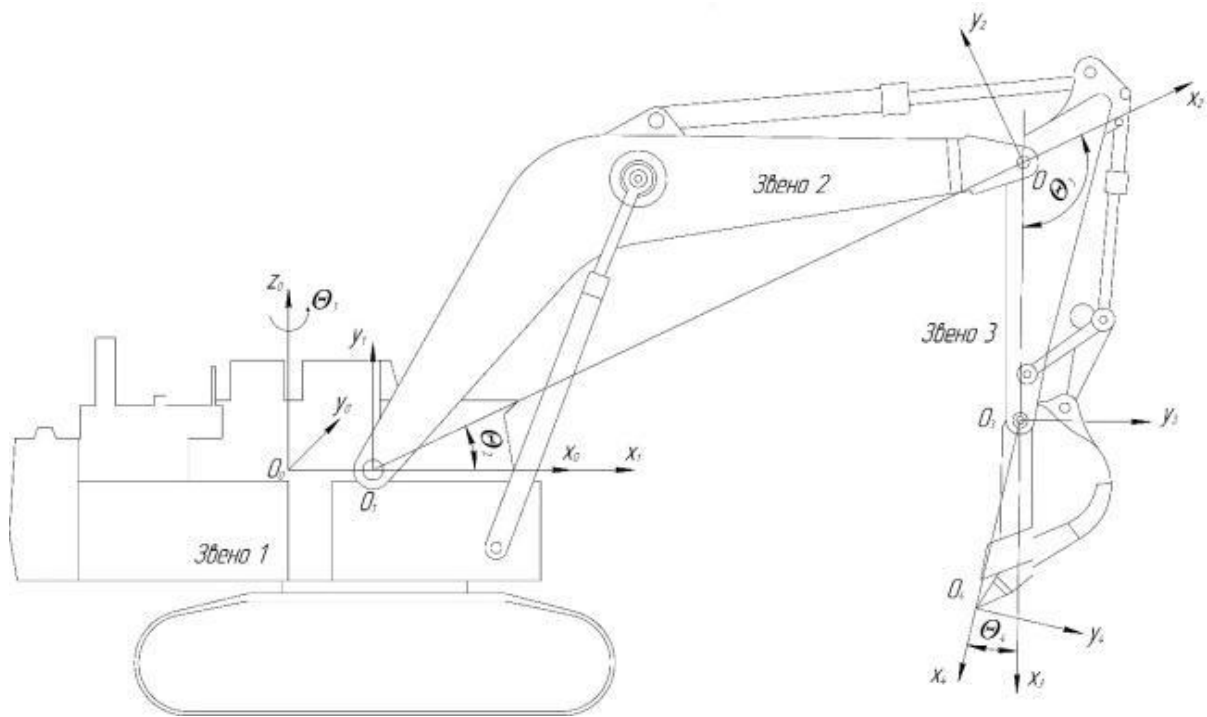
Кинематическая схема гидравлического одноковшового экскаватора типа «обратная лопата»
